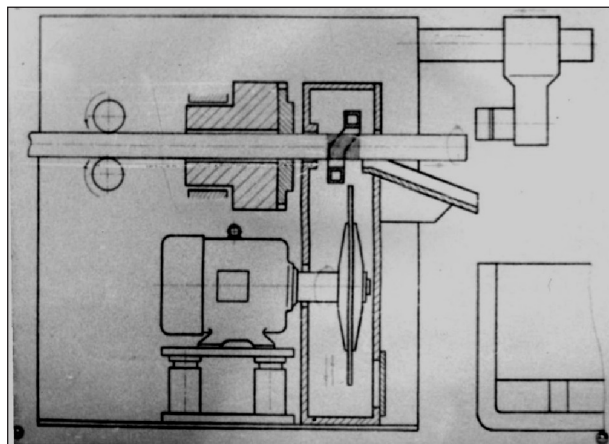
Схема установки для горячей резки труб с нагревом ТВЧ
